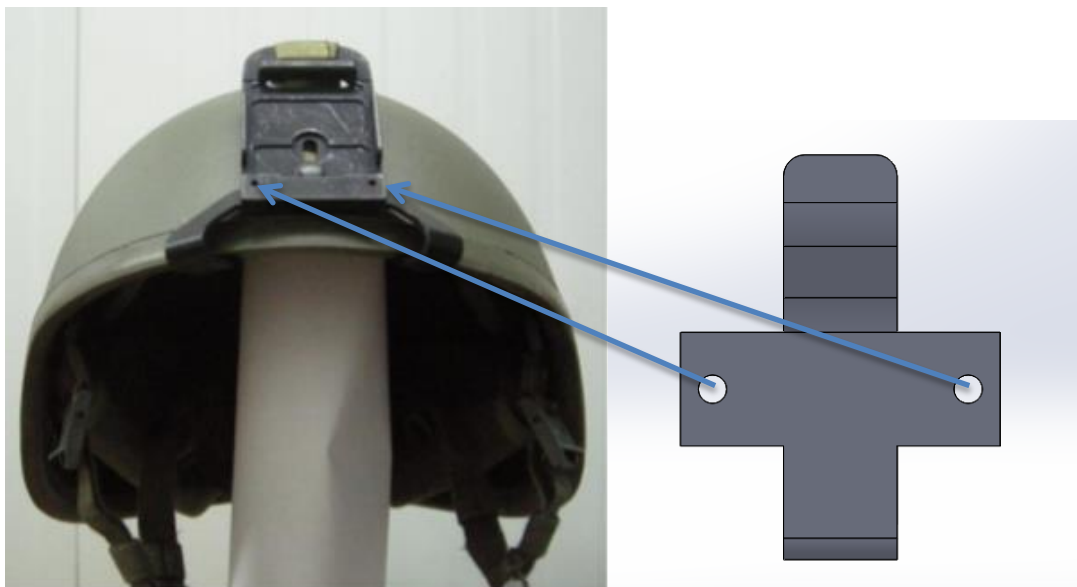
Vista frontal (Izquierda) y alzado (Derecha) del prototipo de la pieza fabricada
